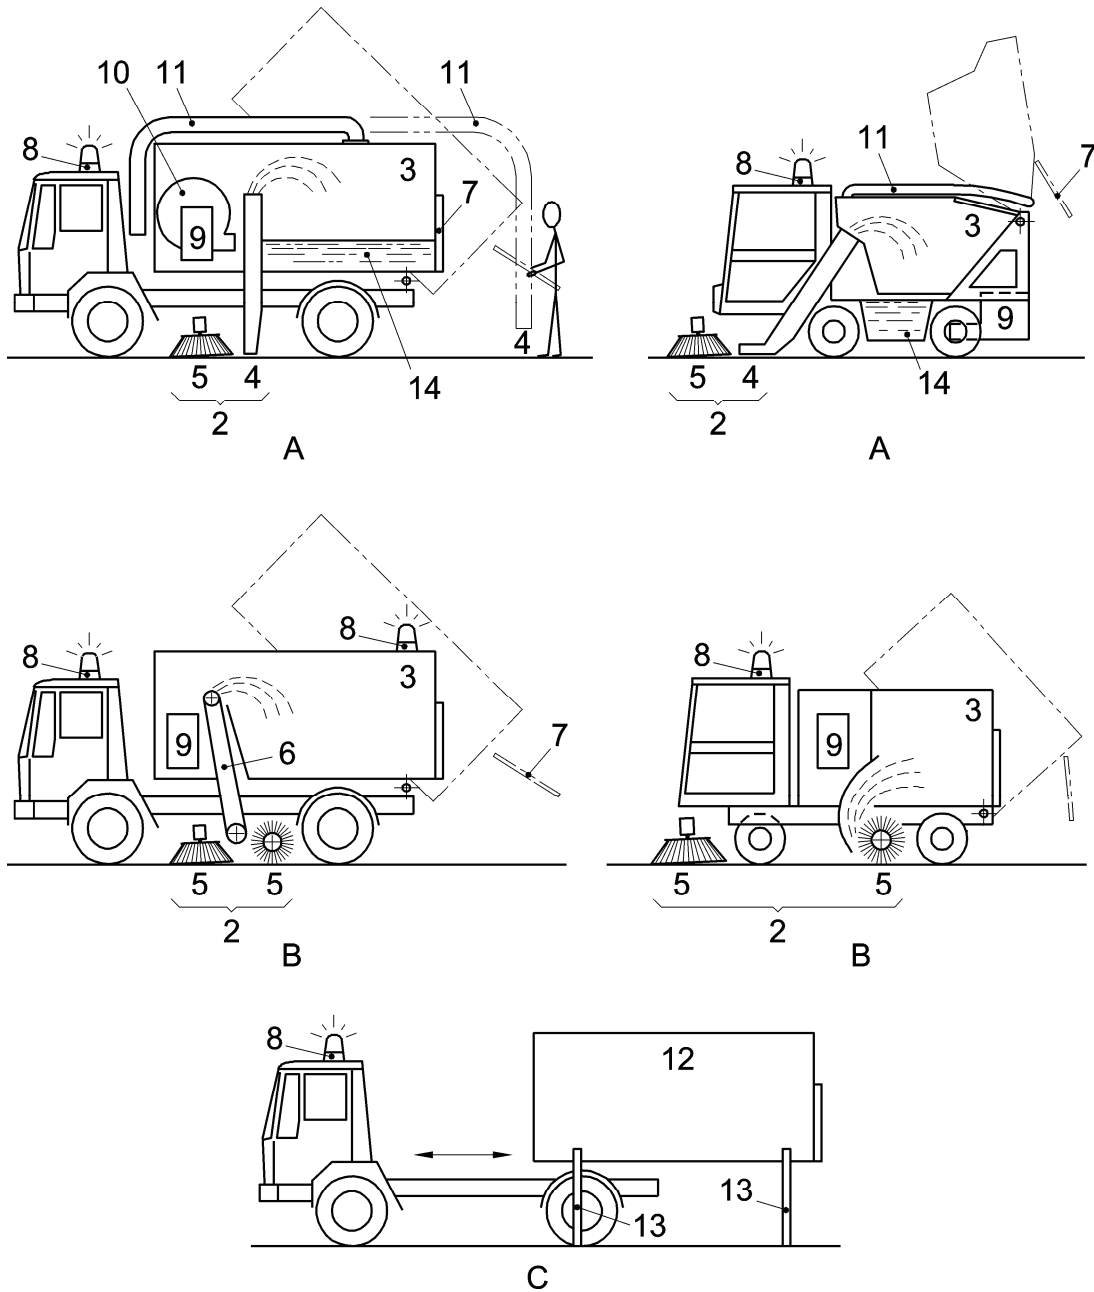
Kehrmaschinen mit Schmutzbehälter
